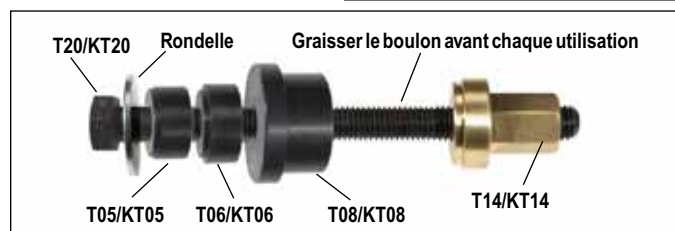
OUTIL DE FIXATION DE LA DOUILLE DANS LA COURTE TIGE DE GUIDAGE
